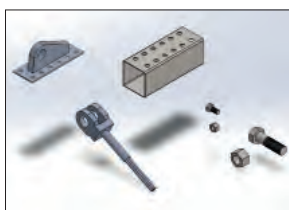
Моделирование узла крепления вант к металлическим элементам
